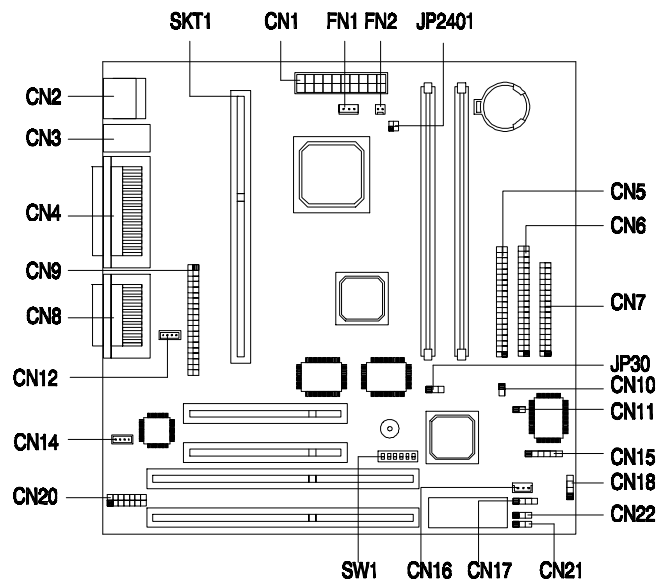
Positionen von Jumper und Steckanschlüssen
